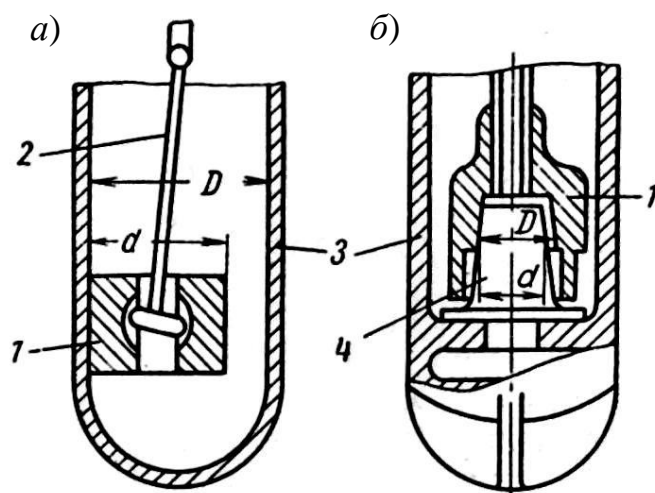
Схемы фрикционно-планетарного вибромеханизма
